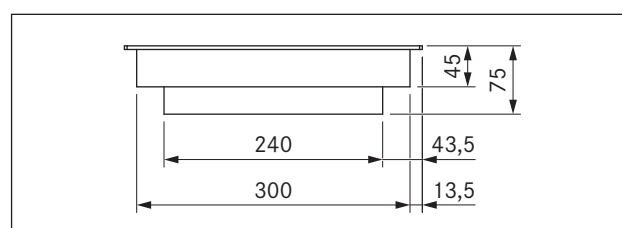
Dimensões do aparelho CKCH, vista frontal
